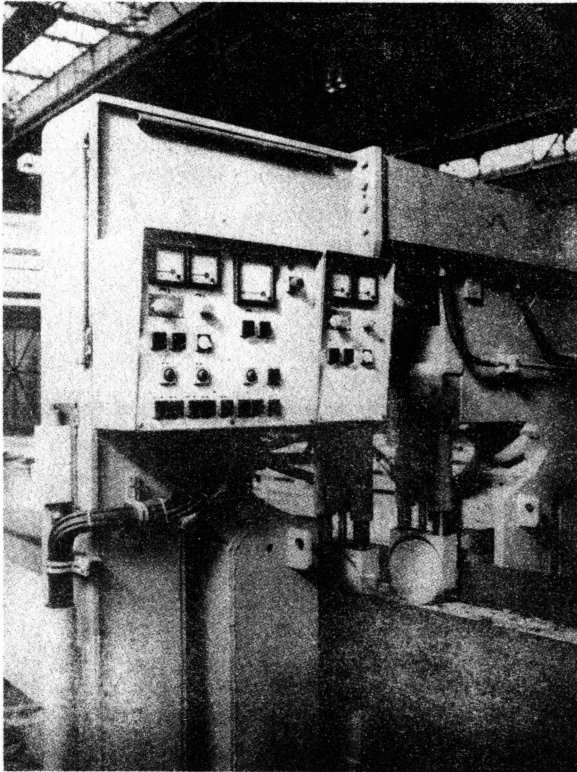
Schweißstation (oben rechts) der Blechträgerdurchlaufschweißanlage
